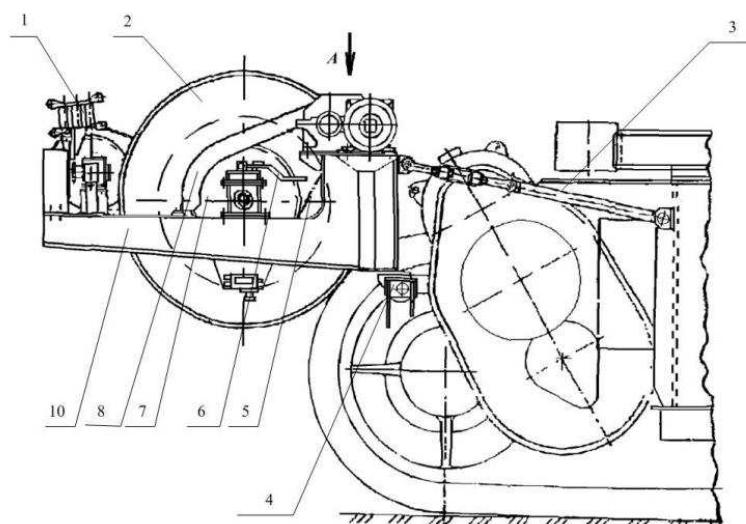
Кабельный барабан (вид сбоку)
